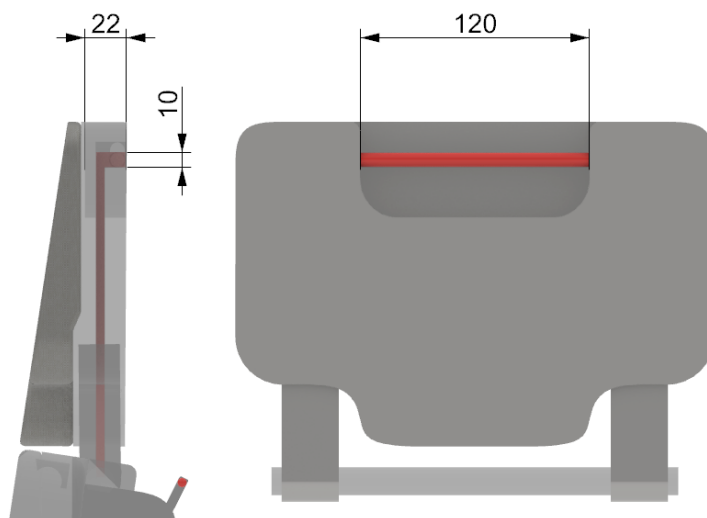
Boční a zadní pohled ovladače mechanismu zajištění opěrky zad (mm)
